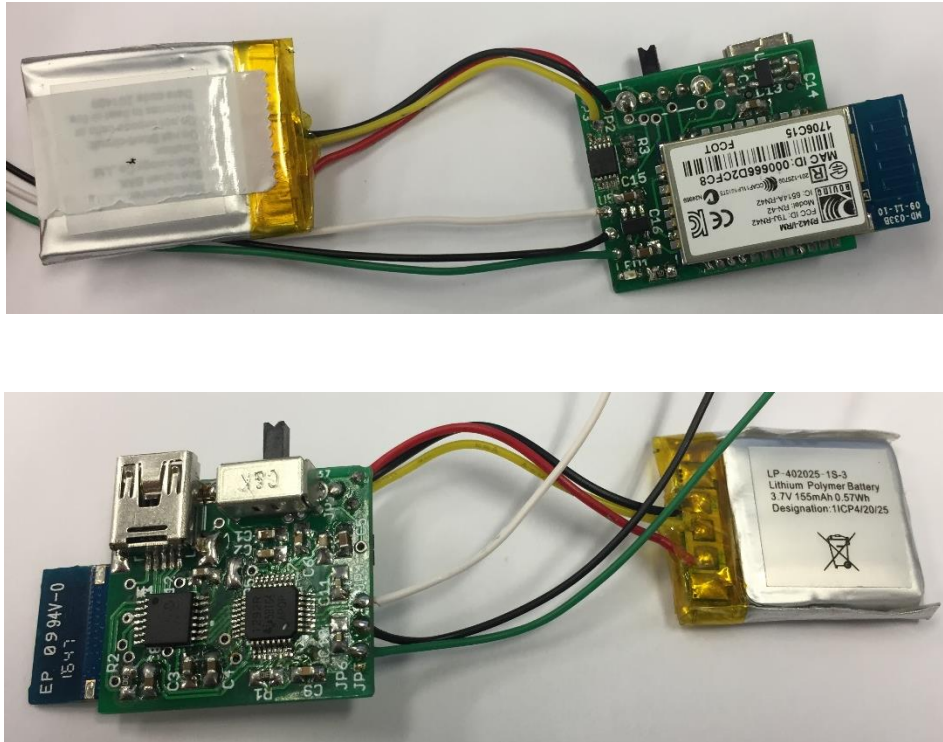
Imagen de las dos capas (TOP y BOTTOM) de la PCB con los componentes soldados.
